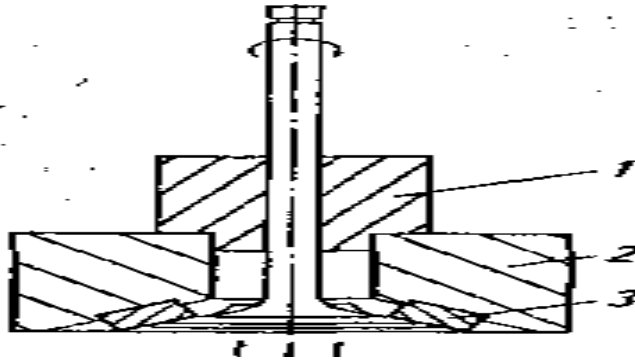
Схема обробки фаски клапана різцевою головкою:
